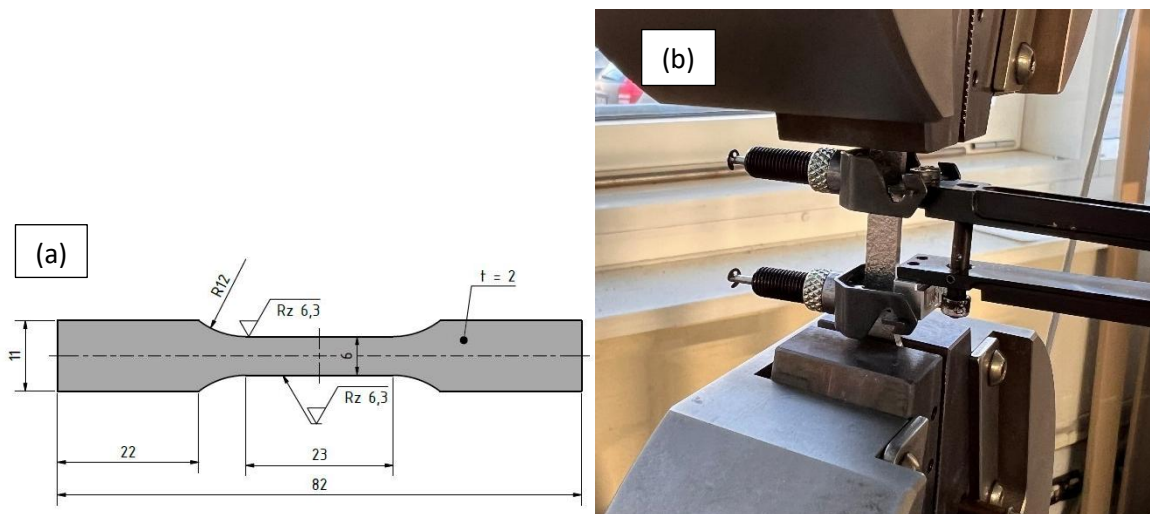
(a) Technische Zeichnung der genutzten Zugproben-Geometrie in Anlehnung an DIN 50125 [262]. (b) Eingebaute Zugprobe aus 1.4462.
